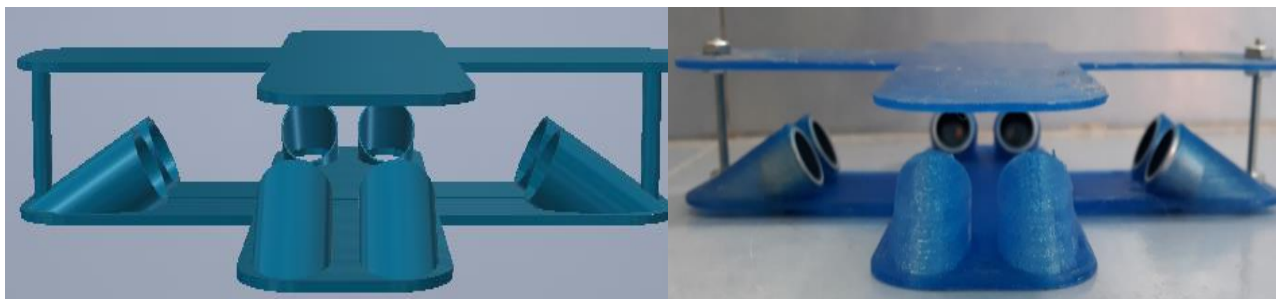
39. Diseño (izquierda) e impresión 3D (derecha) del anemómetro sónico.
